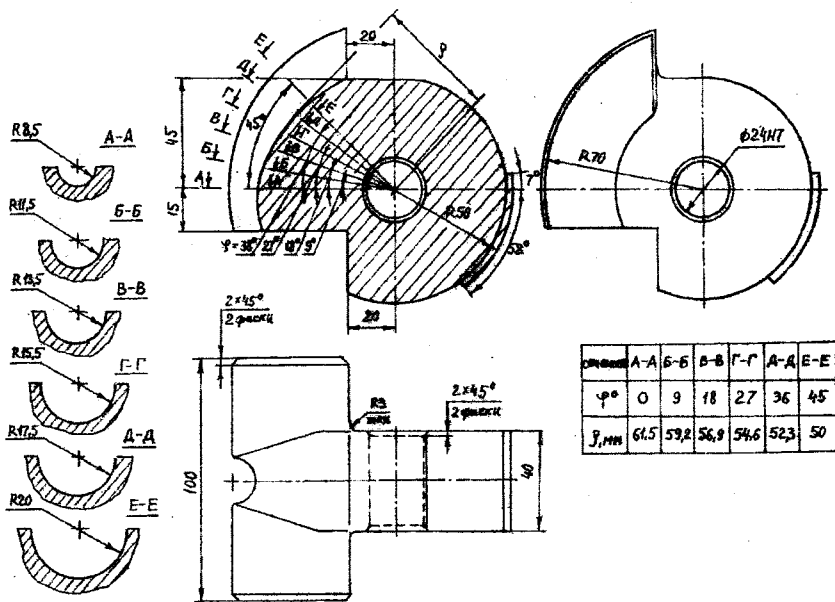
Чертеж вальца, образующего половину полости матрицы штампа
